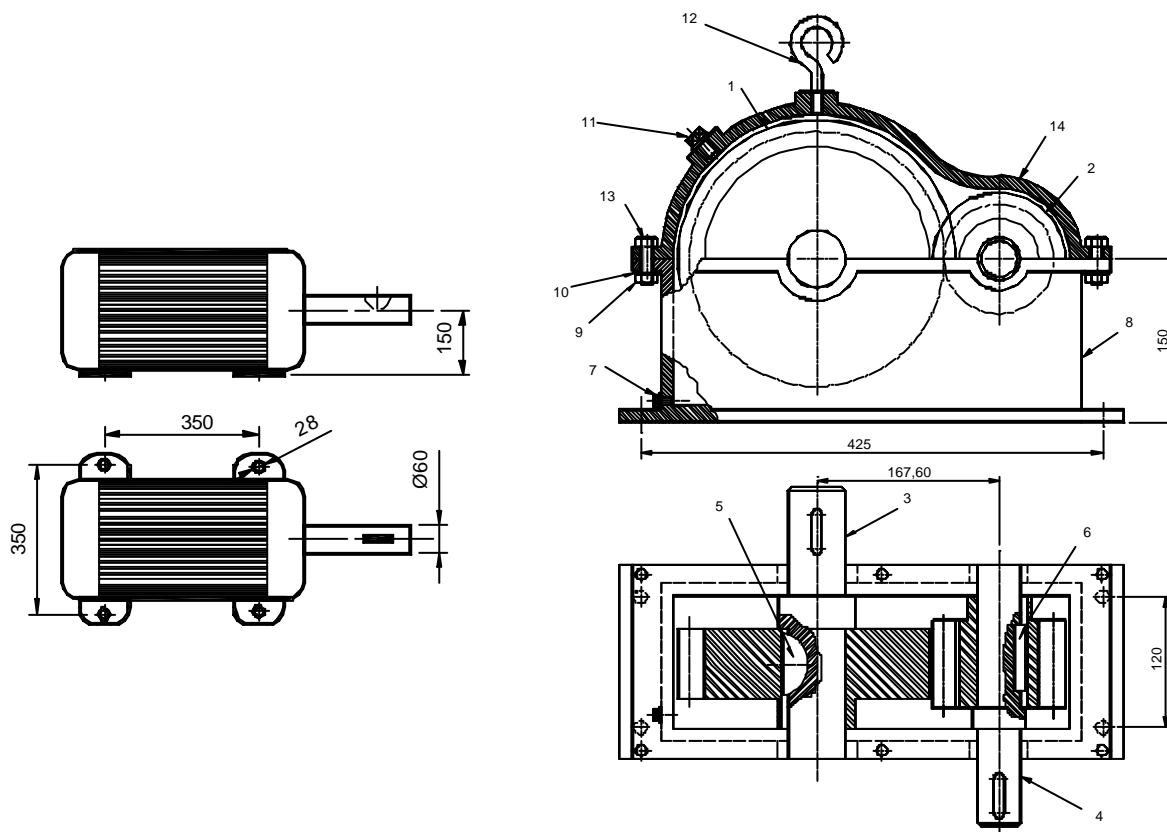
Exemplo de cotação em desenho de conjunto: Motor elétrico e um Redutor
